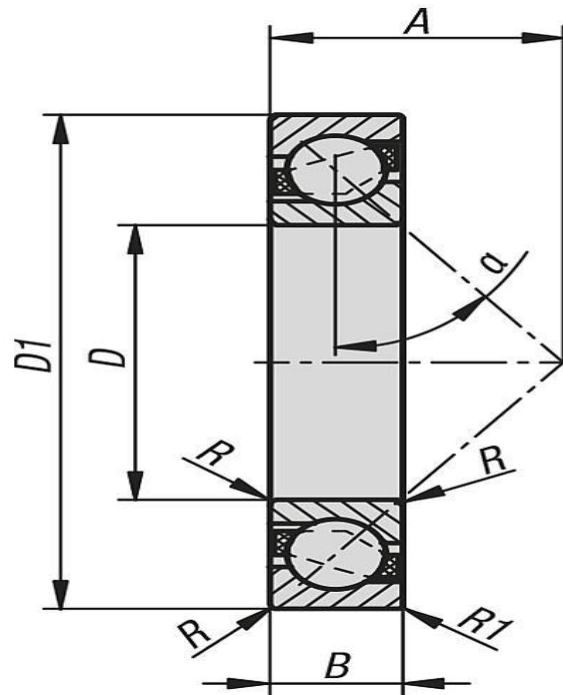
Dessin de définition roulement à bille à contacte oblique
